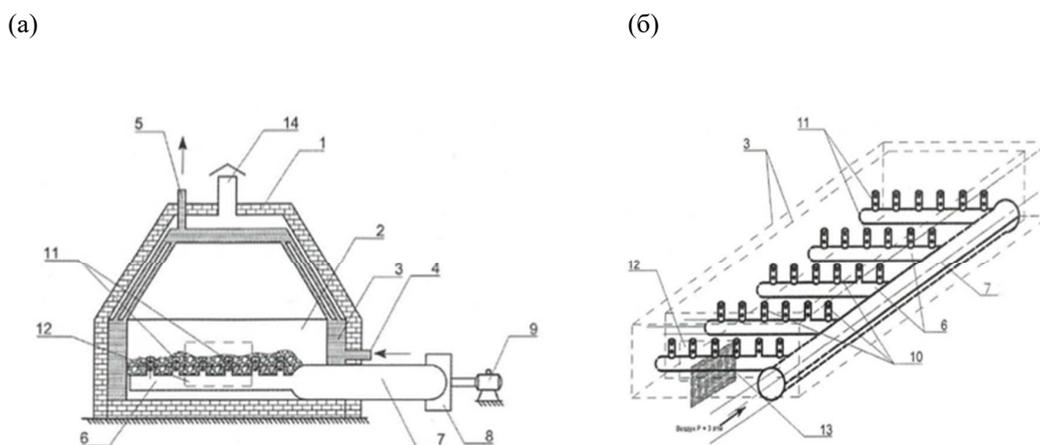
Вертикальный разрез КВТС-0,2 котла (а) и размещение форсунок для подачи воздуха (б): 1 – корпус; 2 – камера сгорания; 3 – емкость с водой; 4, 5 – патрубки подвода и отвода воды; 6 – подача воздуха; 7 – распределитель воздуха; 8 – вентилятор; 9 – электродвигатель; 10 – вертикально установленные форсунки; 11 – радиальные отверстия; 12 – проем для загрузки топлива и очистки от золы; 13 – герметичная дверь; 14 – патрубок для удаления продуктов сгорания.
